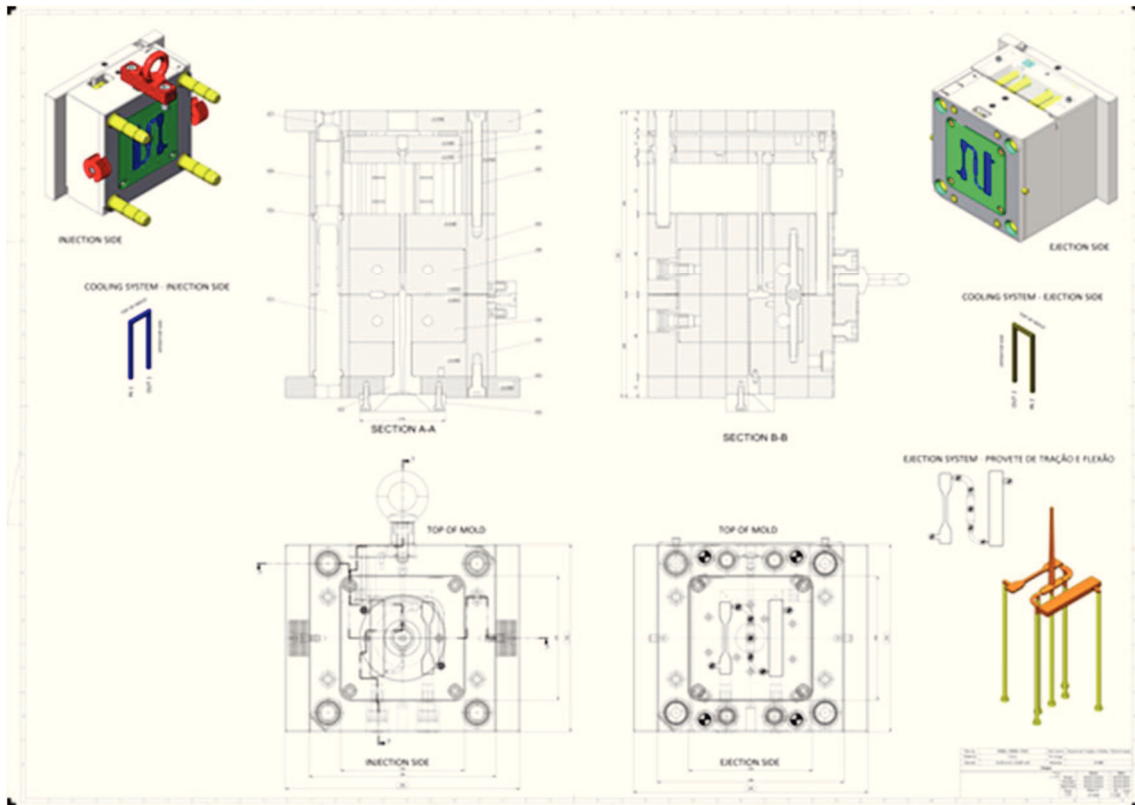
Desenho esquemática em desenho 2D, relativo ao molde dos provetes.
